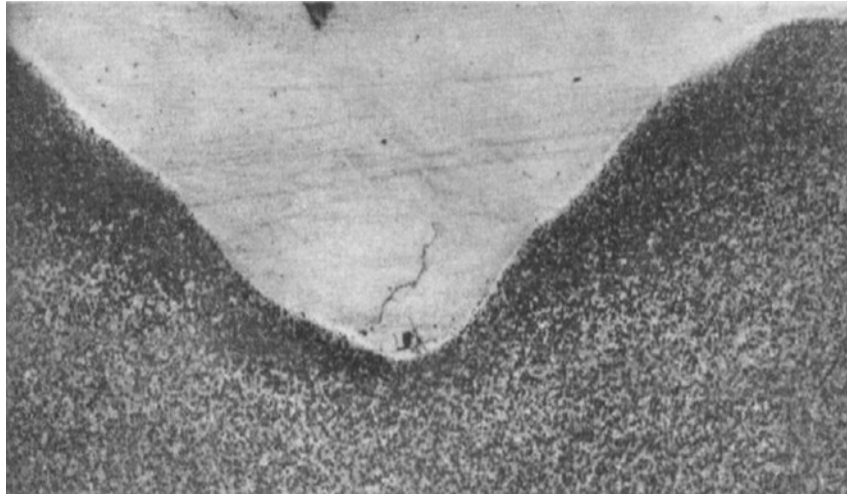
Гаряча тріщина в наплавленому металі магнієвої деталі, x3 [2]
